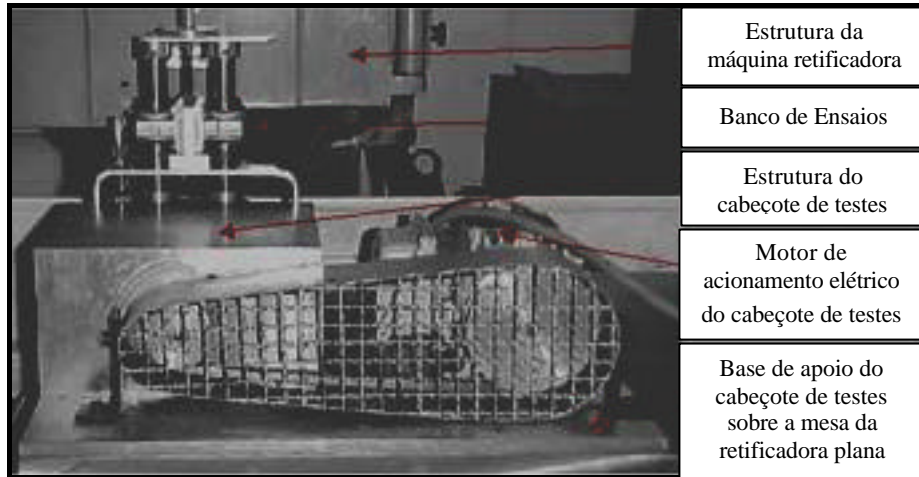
Fotografia do conjunto banco de ensaios – cabeçote de testes, juntamente com o motor de acionamento, posicionados sobre a mesa da máquina retificadora
